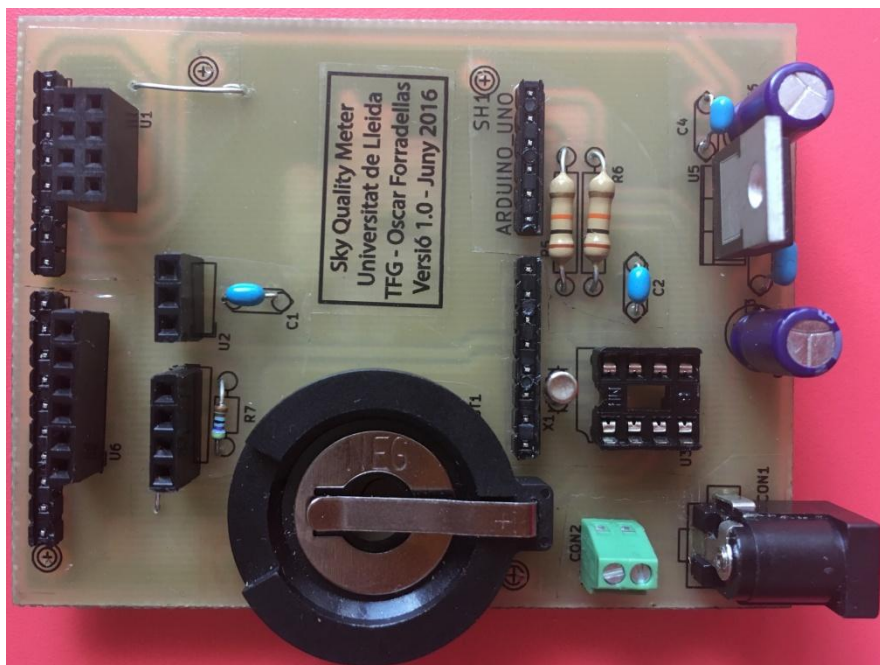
PCB finalitzat a falta del cablejat i afegir algun integrat
